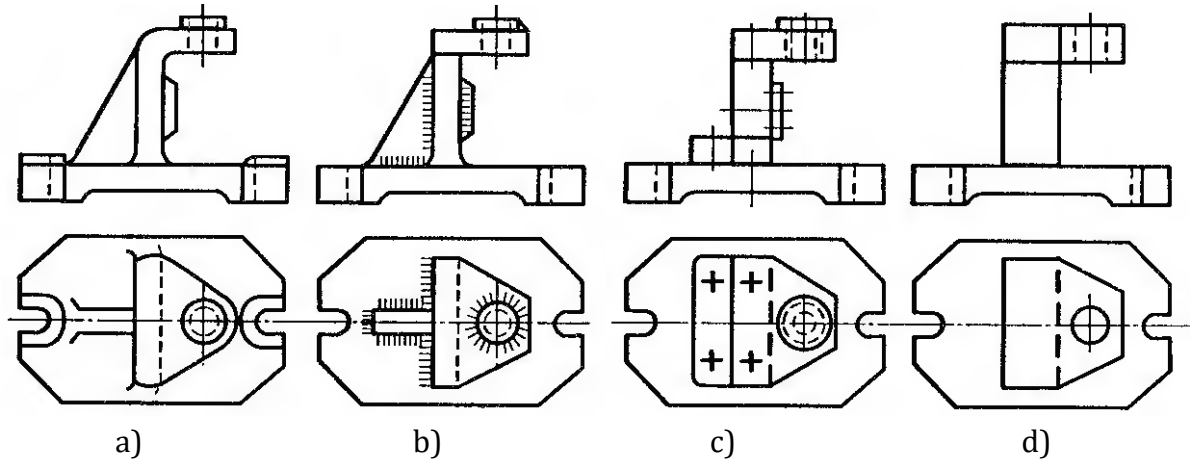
Варианты конструкции корпусов приспособлений: литого (а), сварного (б), сборного (с), кованого (д)
